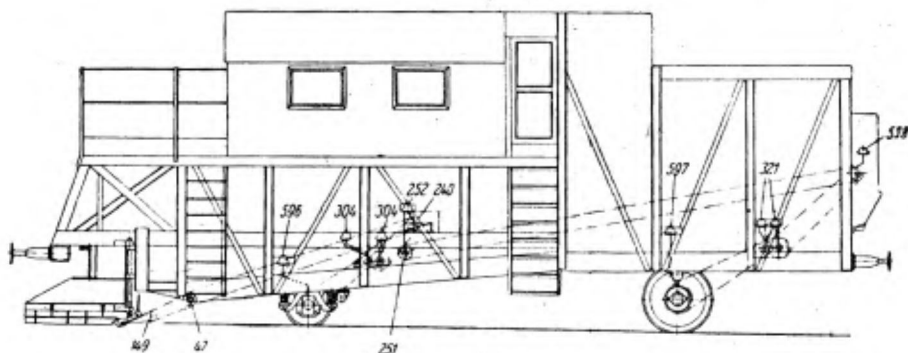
Схема смазки кулачковых муфт и редукторов головной машины
